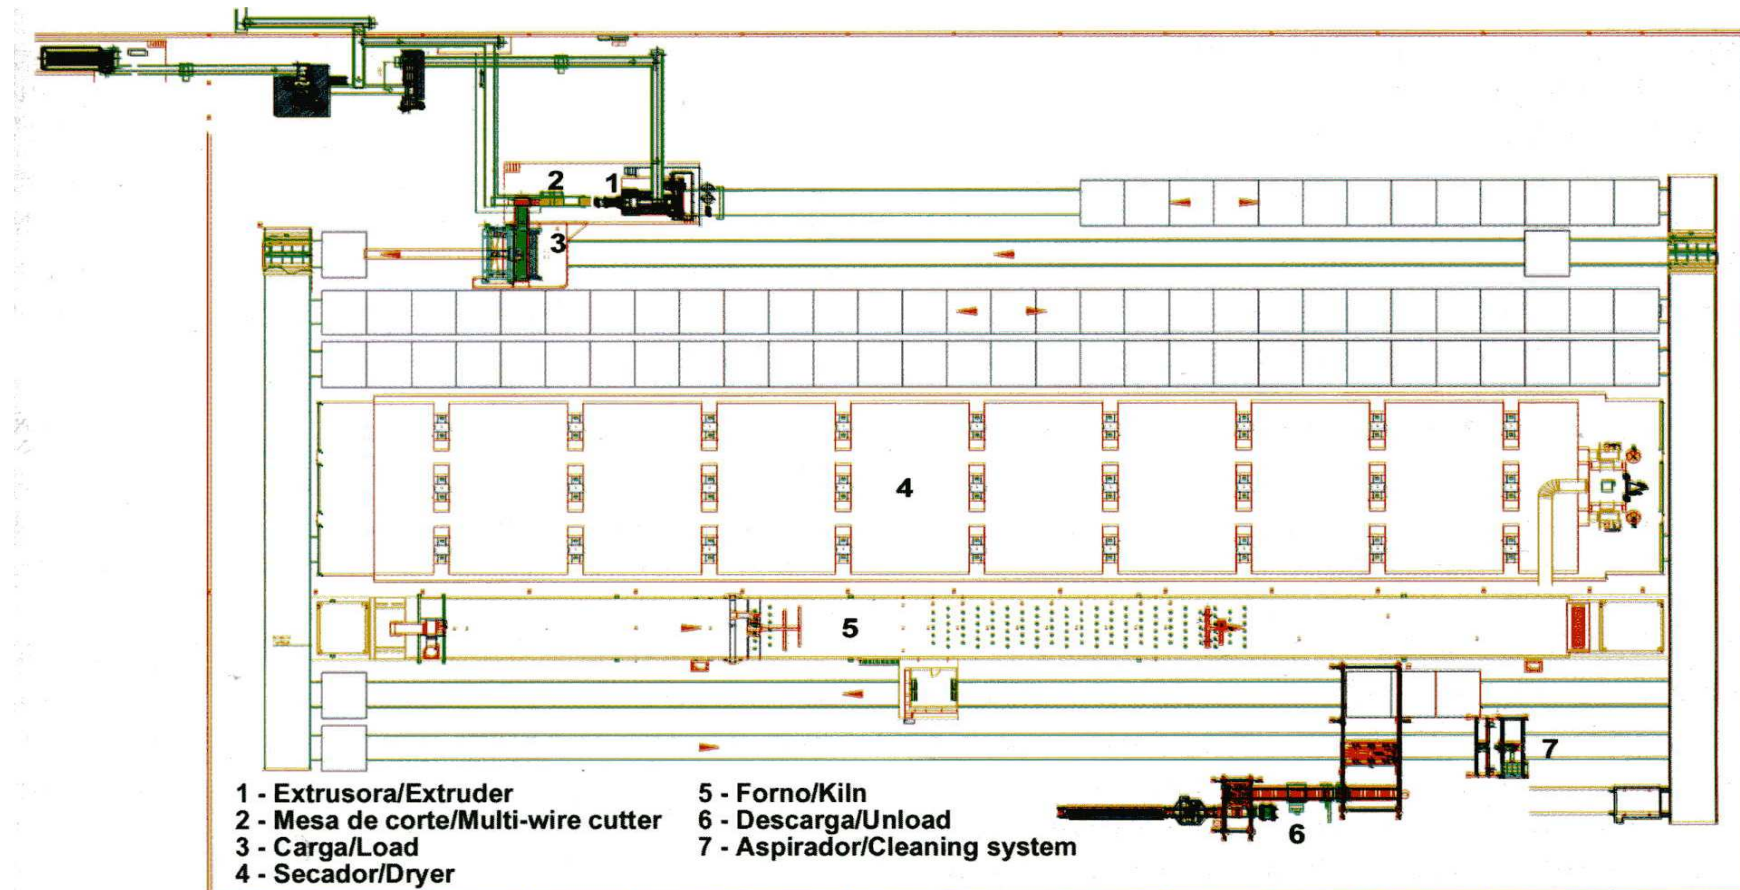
Layout do processo de fabricação de tijolo⁸
